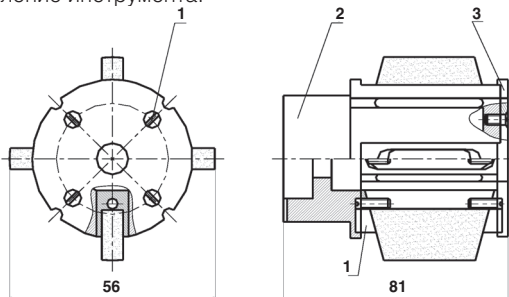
Сборный абразивный круг: 1 — абразивный сегмент, 2 — корпус, 3 — крышка, 4 — винты.
